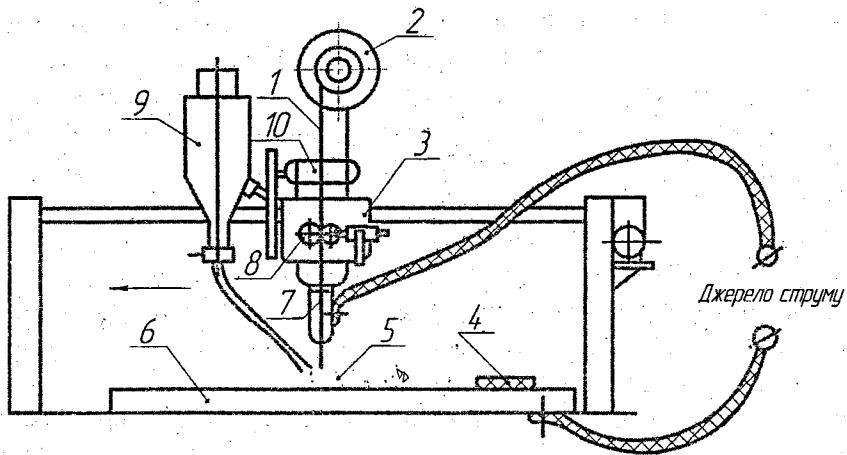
Схема автоматичного зварювання (наплавлення) під шаром флюсу:
